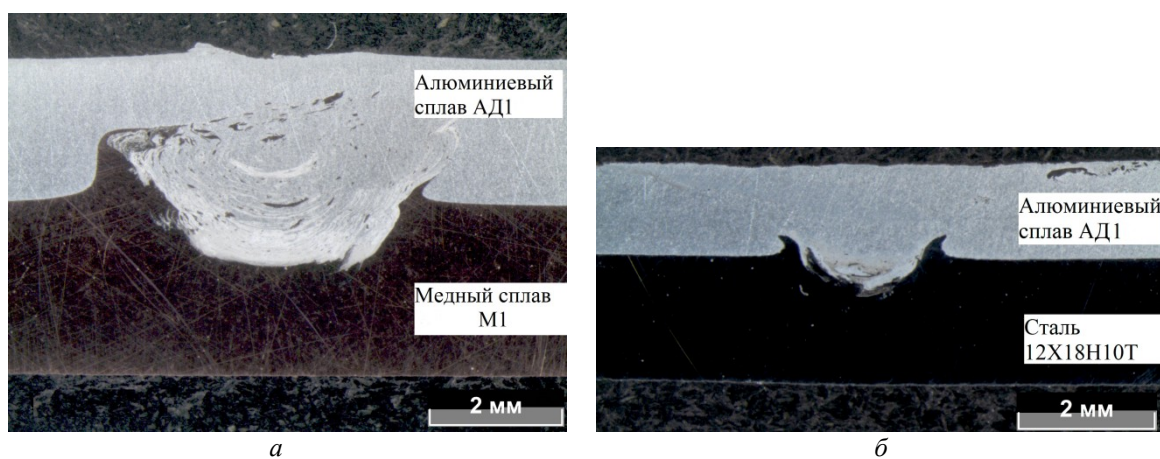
Внешний вид сваренных образцов алюминиевого АД1 и медного М1 сплавов:
